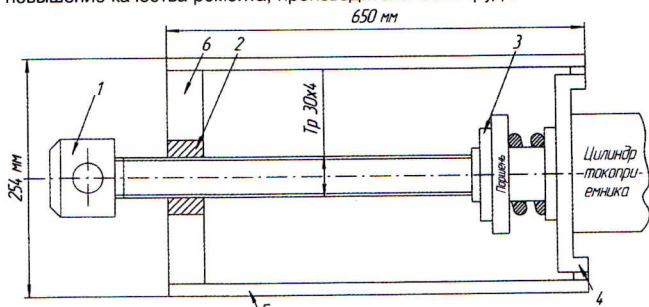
Приспособление для разборки цилиндра токоприемника: 1 — винт; 2 — упор; 3 — упор; 4 — захват; 5 — щека; 6 — тяга
